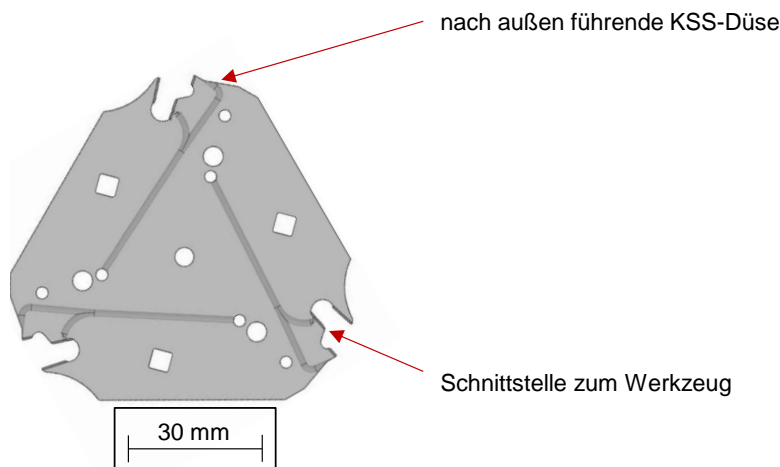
CAD-Modell des microCutOff-Werkzeughalters mit innenliegenden Kühlkanälen
